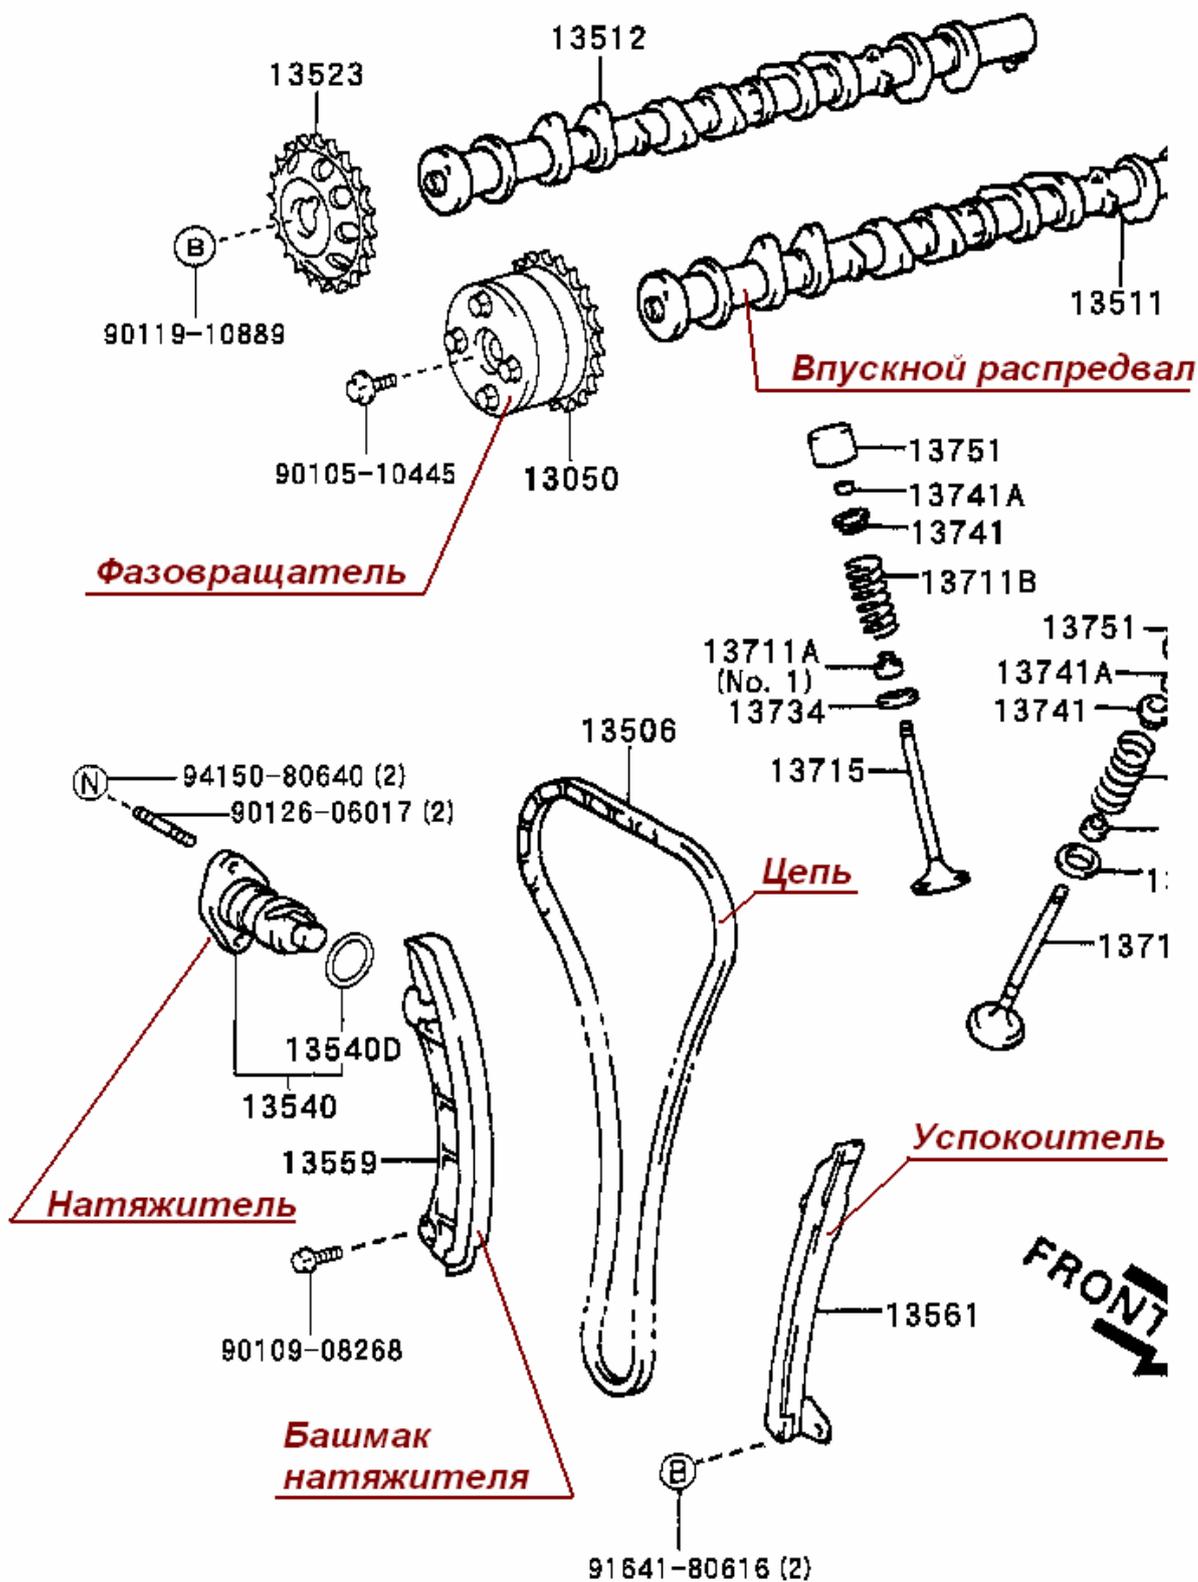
Схема механизма привода ГРМ двигателя Toyota 1ZZ.
